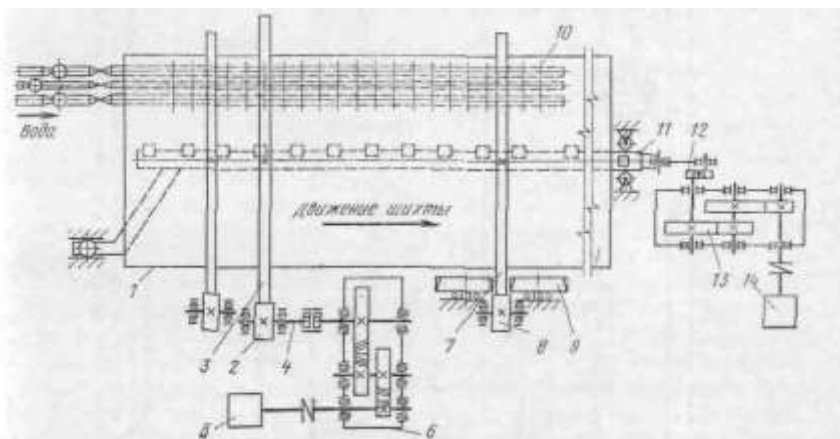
Кинематическая сема привода барабанного смесителя
